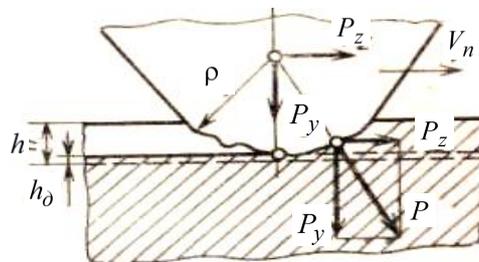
Схема действия абразивного зерна на обрабатываемую деталь
